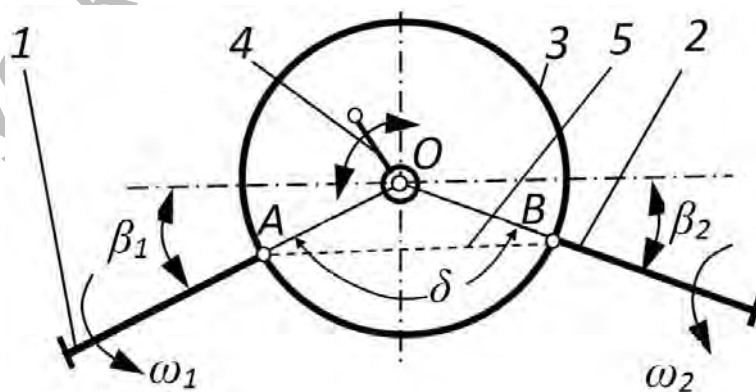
Кинематическая схема механизма: 1 – ведущий вал; 2 – ведомый вал; 3 – reduцирующий механизм; 4 – механизм поворота и фиксации корпуса редуктора относительно лап; 5 – условный карданный вал
